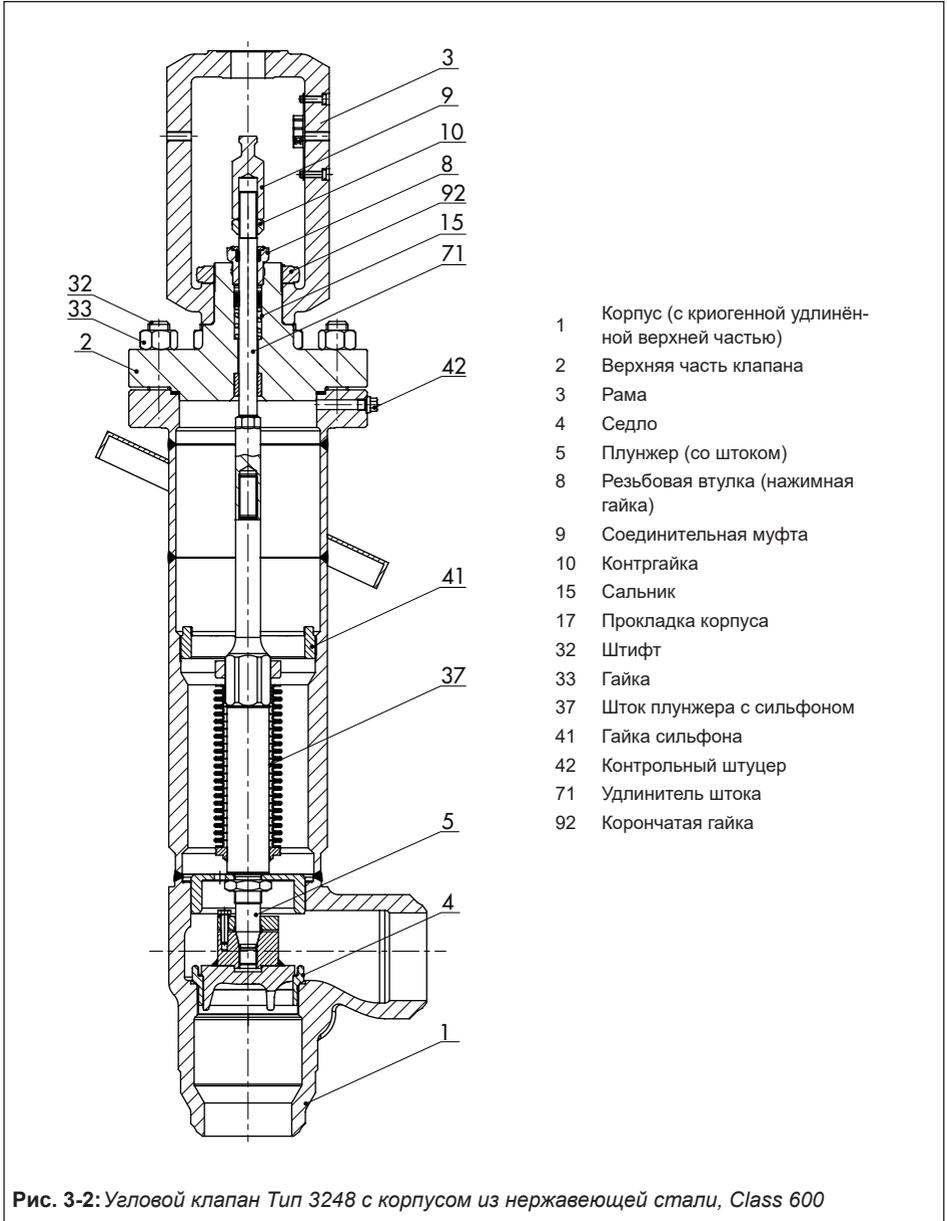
Угловой клапан Тип 3248 с корпусом из нержавеющей стали, Class 600
